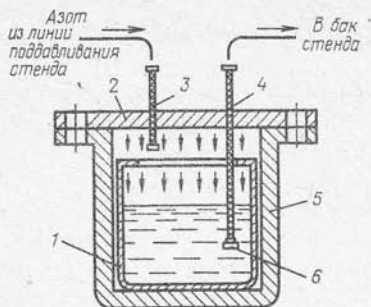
Схема приспособления для заправки баков стенов из тары завода-поставщика: 1 — тара; 2 — крышка гермокамеры; 3, 4 — шланги (3 — для подачи азота, 4 — для подачи жидкости в бак стенов); 5 — корпус гермокамеры; 6 — фильтр
